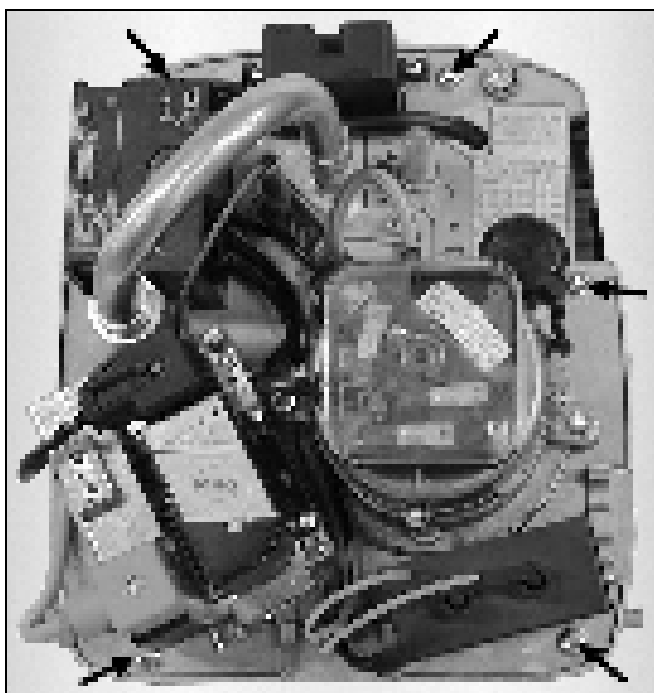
Крышка корпуса с 5 быстрозакручивающимися винтами
